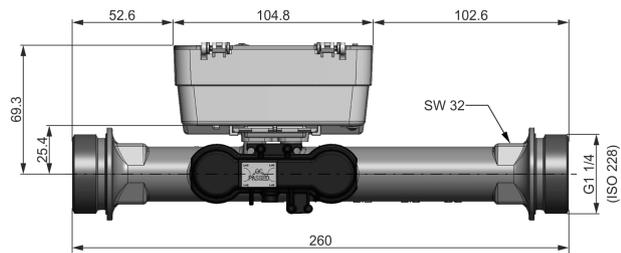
WSx8xx_Massbild_260mm_1 Abb. 5: Übersicht Masse Baulänge 260 mm (Gewinde)
